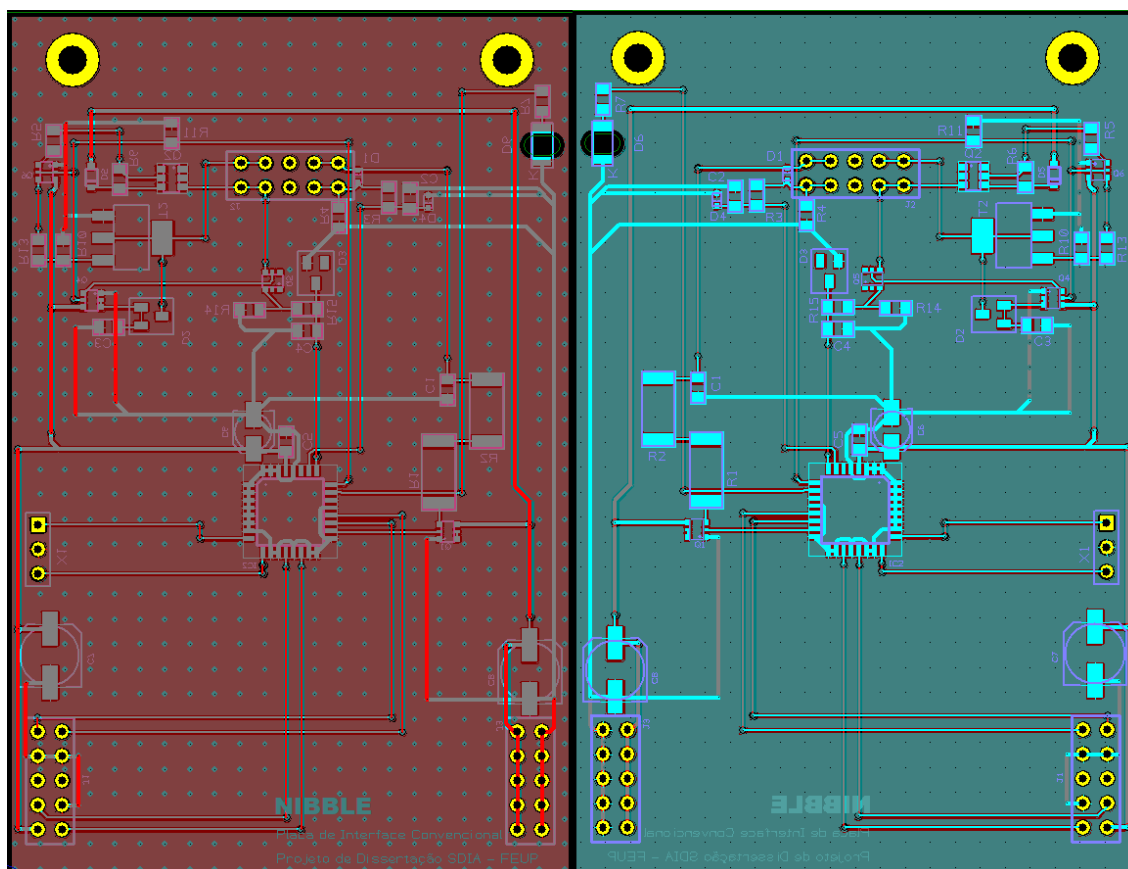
Vista superior e inferior do PCB da Placa Convencional
